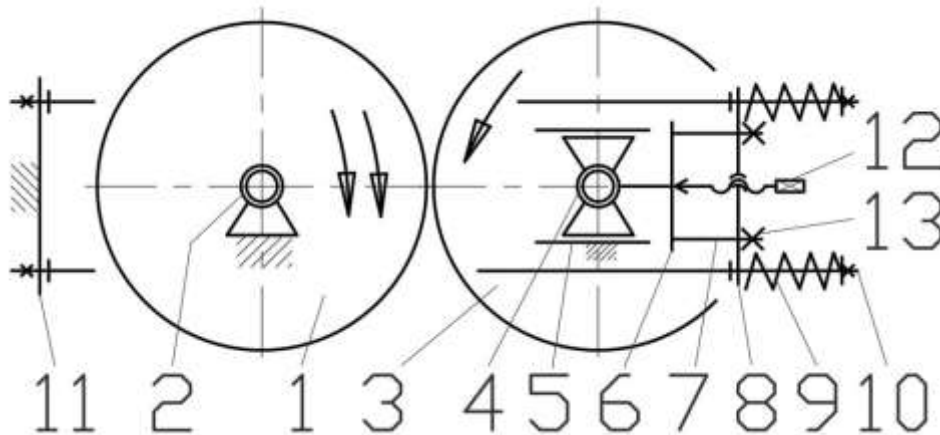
Схема двухвалковой дробарки.
